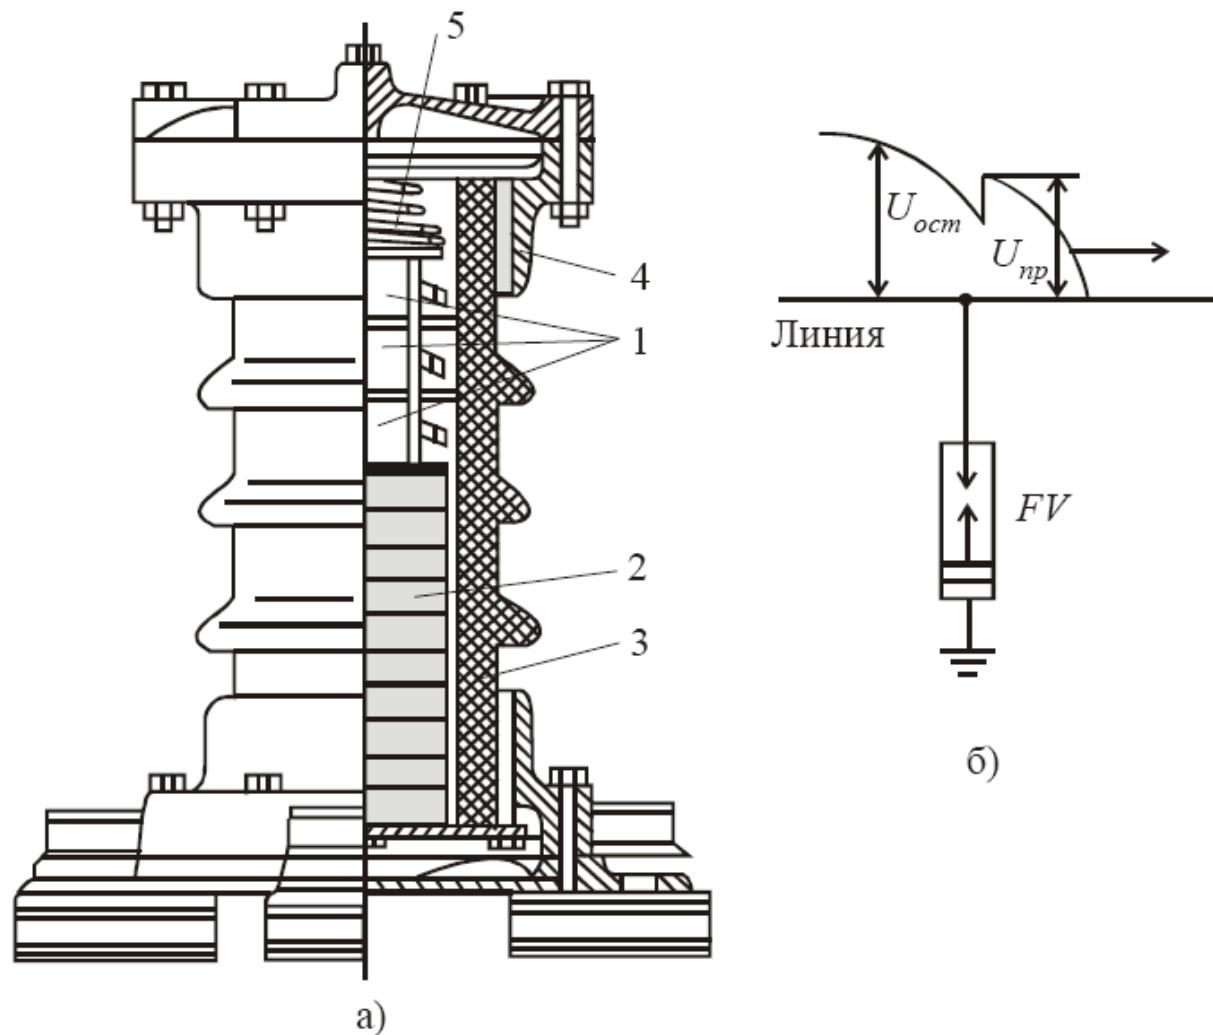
Вентильный разрядник: а) общий вид; б) схема включения. 1 – искровые промежутки; 2 – вилитовые (тервитовые) диски; 3 – фарфоровый корпус; 4 – крышка; 5 – пружина.
